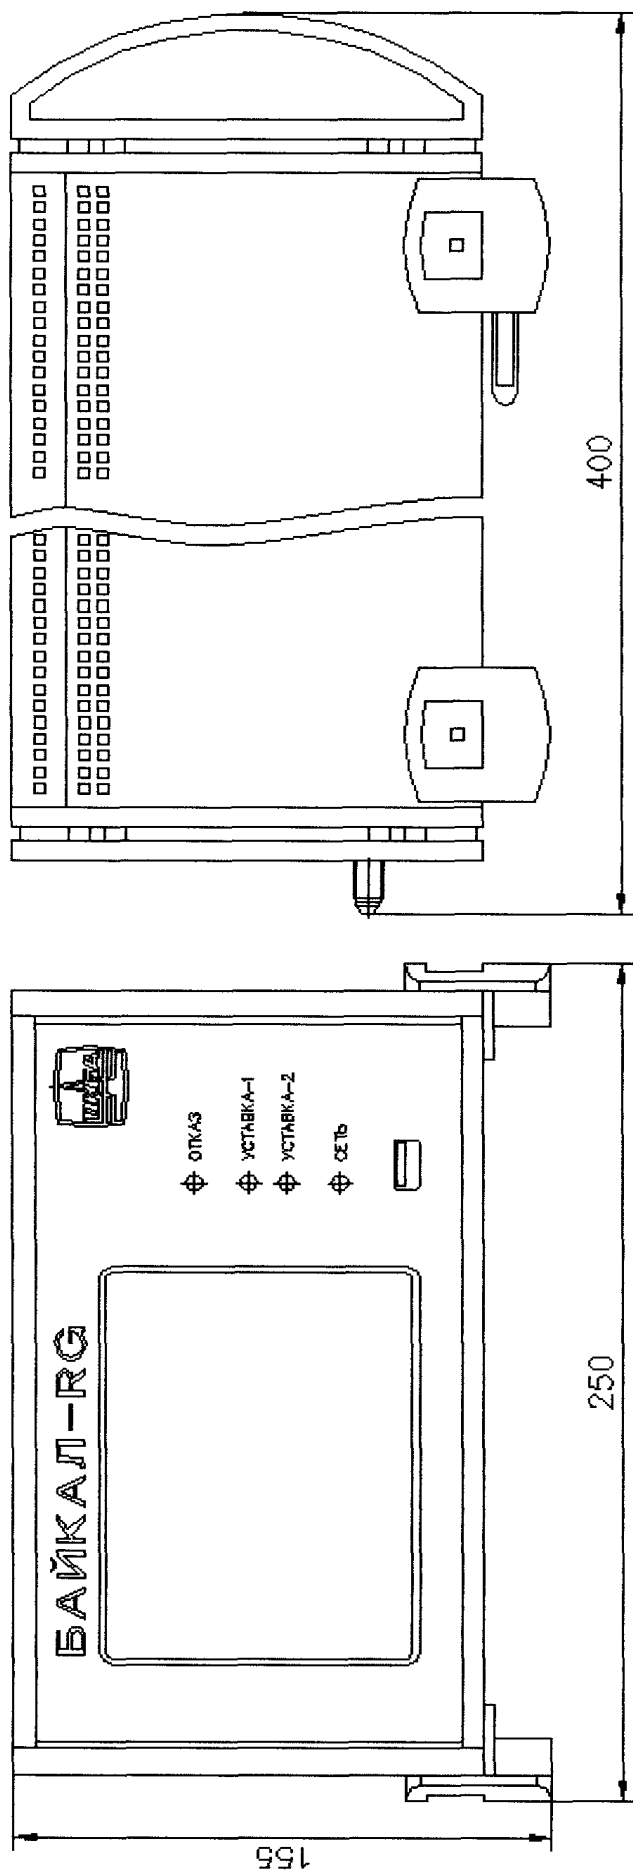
Габаритный чертеж гигрометра БАЙКАЛ-РГ
